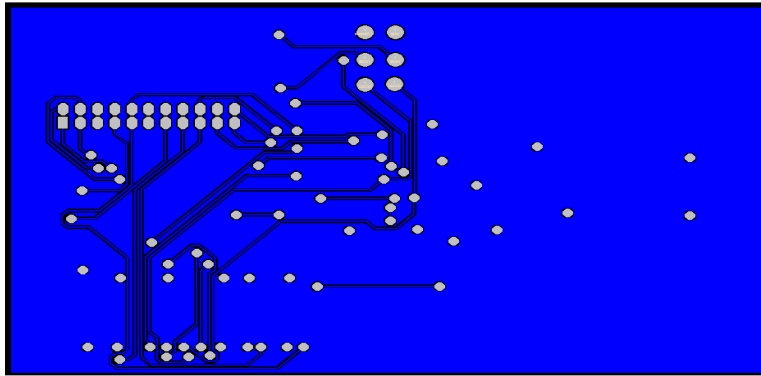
PCB fresado para el montaje de la etapa de radio (Bottom Layer).
